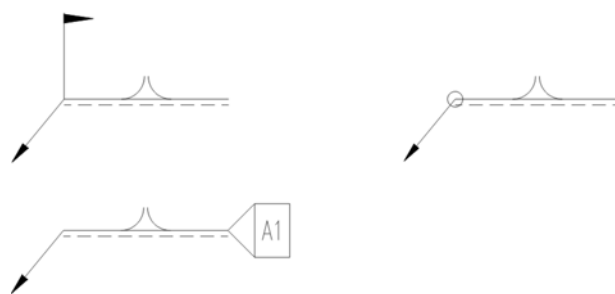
Символ сварки (монтажная сварка, сварка по периметру, с привязкой)
